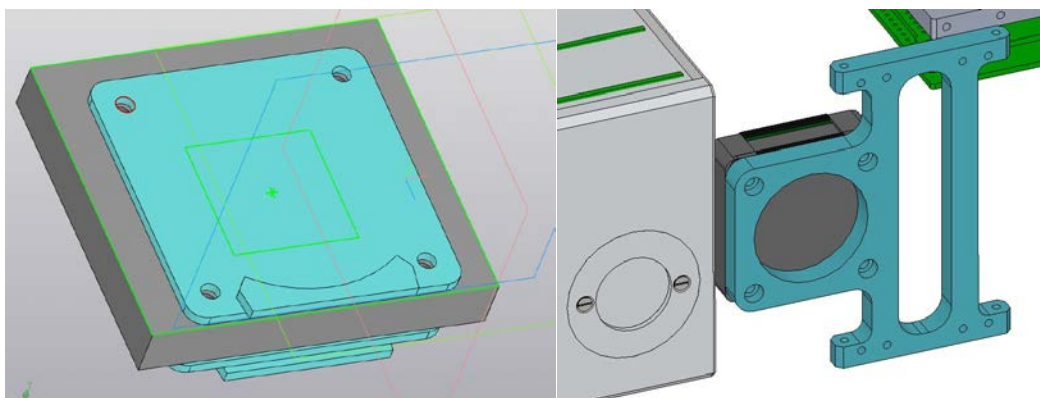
Детекторный блок прибора МАДИЗ – сборка из двух CMOS матриц.
